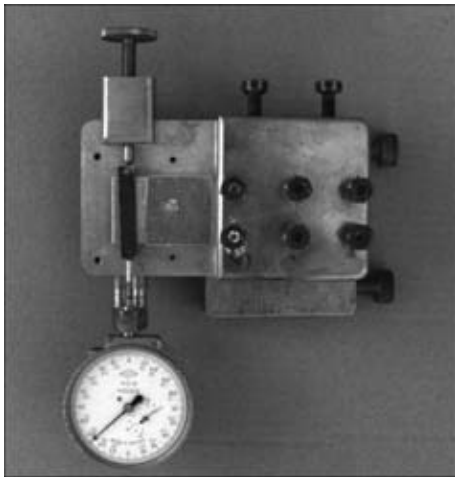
Загальний вигляд навантажувального пристрою для визначення діаметра ядра зварної точки з використанням механічного навантаження
